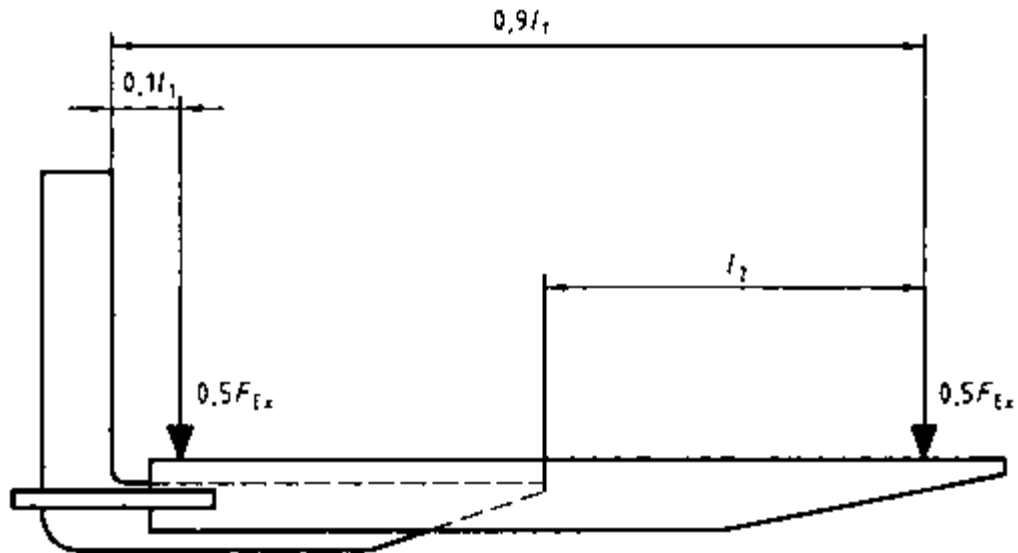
Двойное приложение испытательной (расчетной) нагрузки для открытого и закрытого сечения удлинителя вила
